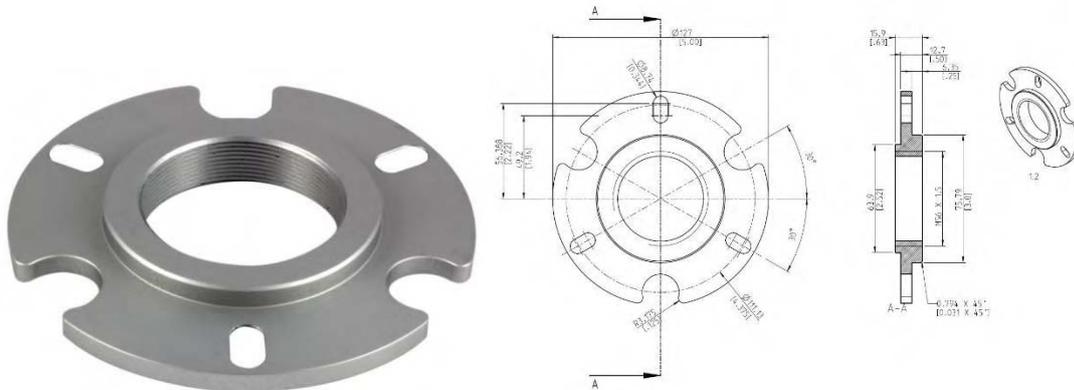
Vue et dimensions du flasque de montage (E-MF-7)
